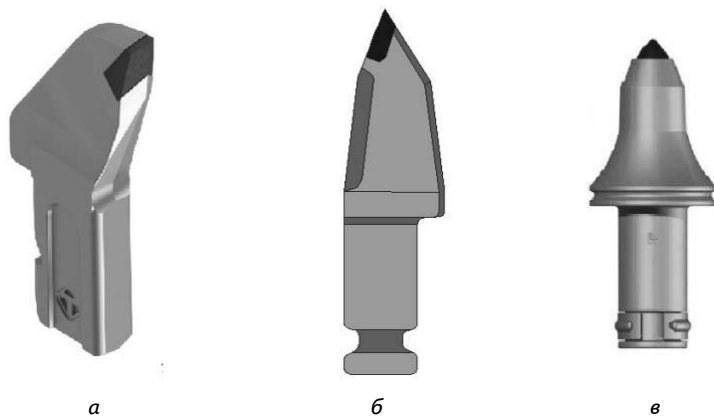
Типы резцов очистных комбайнов¹: а — радиальный; б — тангенциальный неповоротный; в — тангенциальный поворотный
